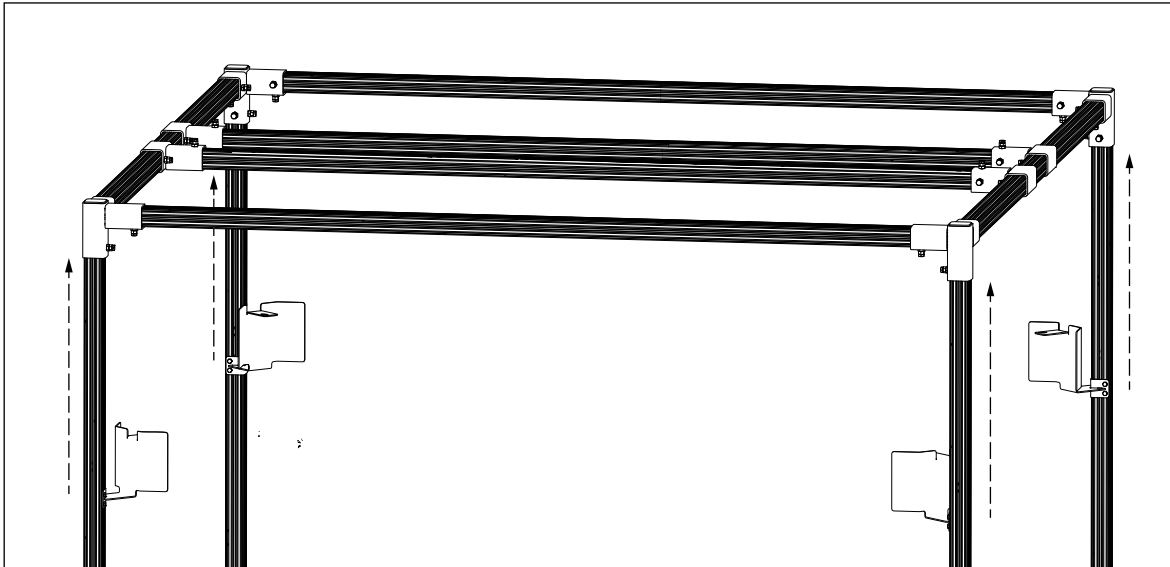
Montage der Schutzvorrichtungen für die remoten IFM-Sensoren
